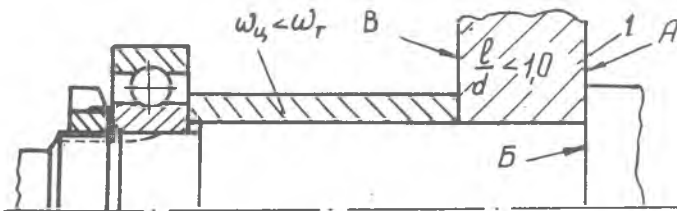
Установка на валу колеса с короткой ступицей, втулки и подшипника
